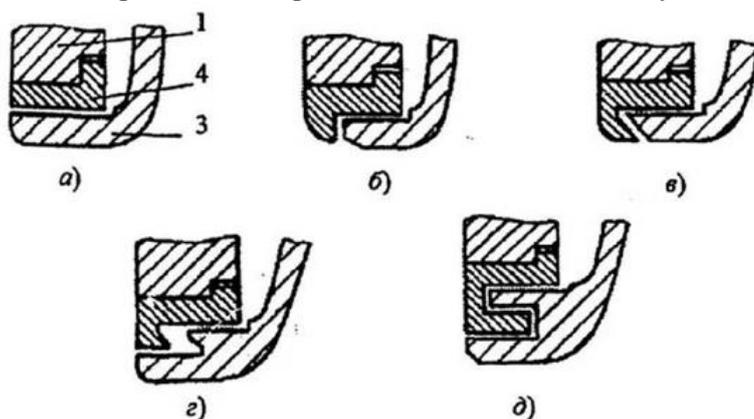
Конструктивные схемы уплотнений рабочих колес: 1-копус секции; 3 - рабочее колесо; 4 - уплотнительное кольцо
